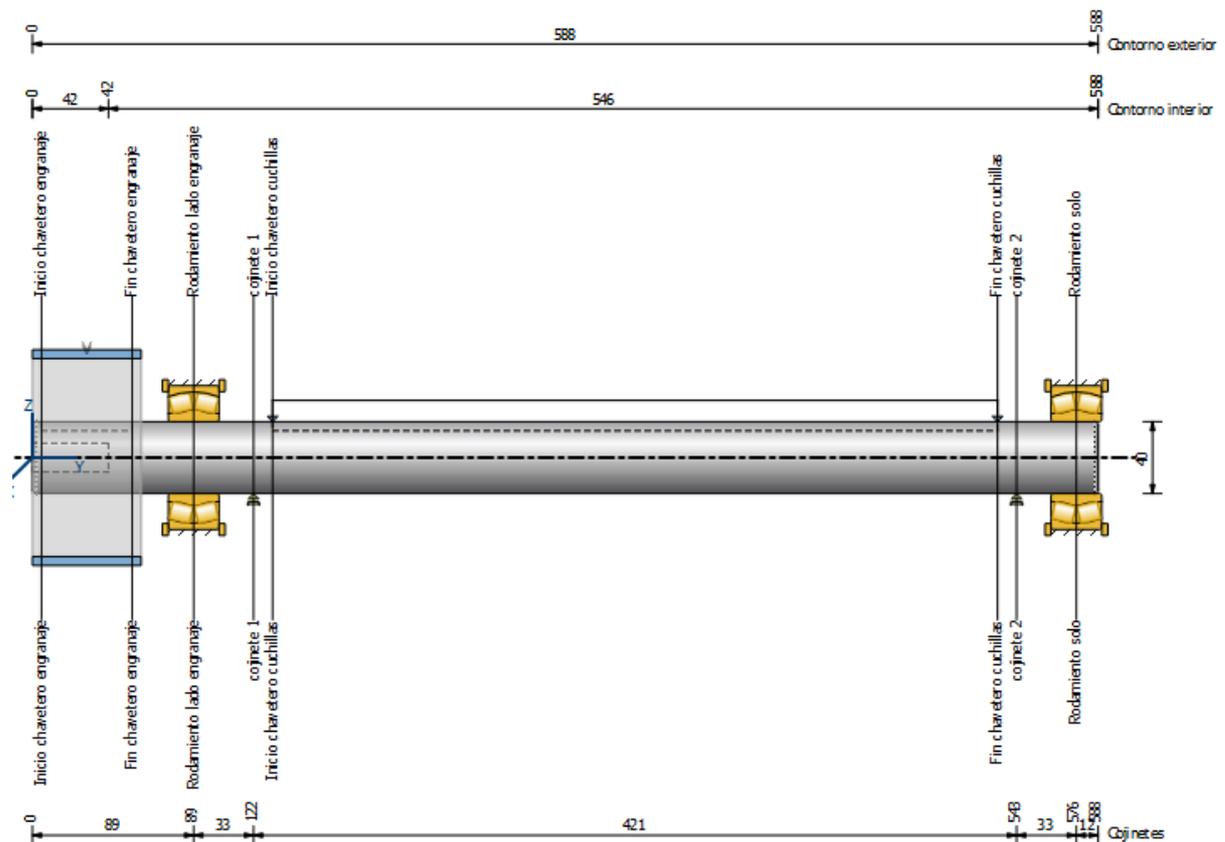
Diseño y dimensiones del árbol de cuchillas con sus rodamientos y cojinetes.
